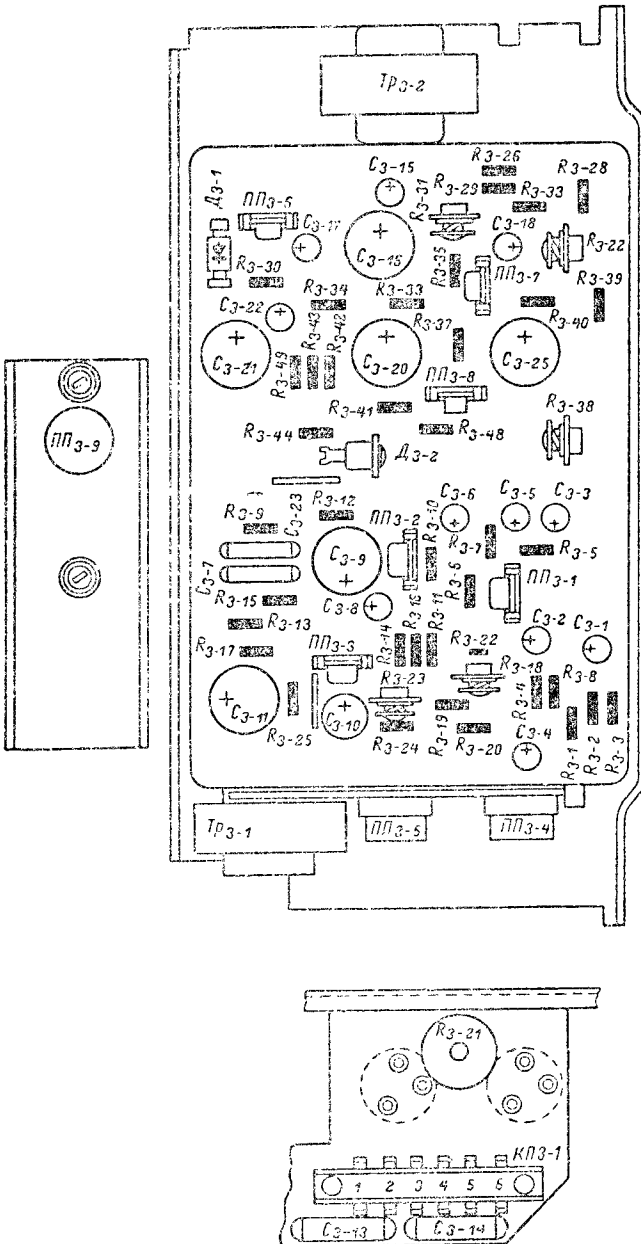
Блок УНЧ и кадровой развертки телевизора «Вечер» (вид со стороны деталей).
